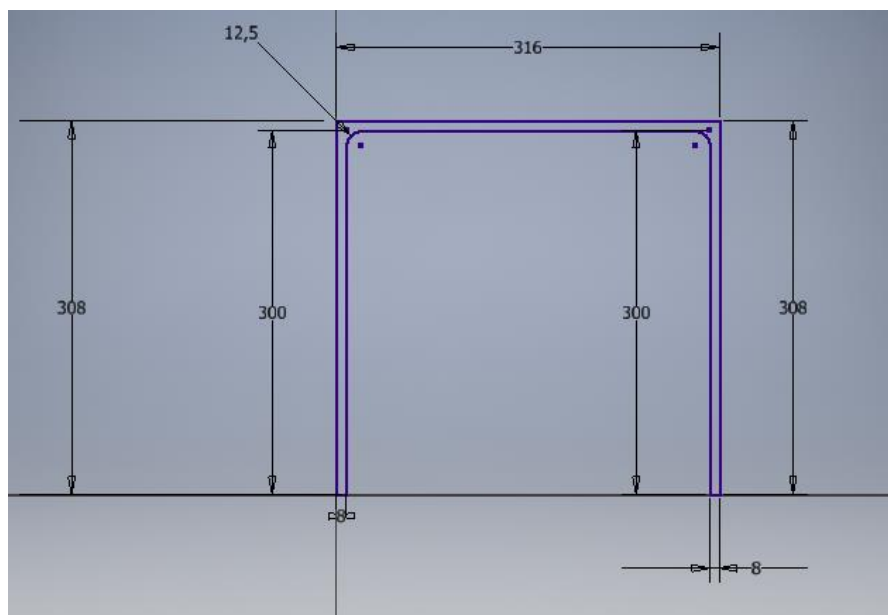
Conjunto de la estructura. Fuente: Autodesk Inventor.
